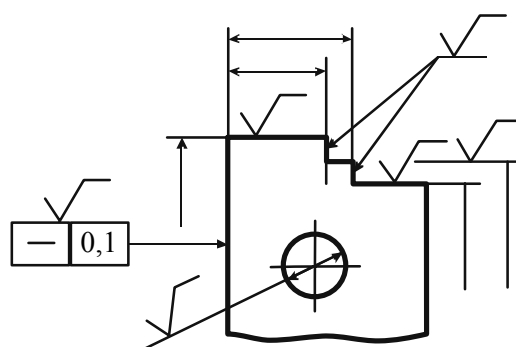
Пример обозначения шероховатости поверхностей на размерных или выносных линиях
